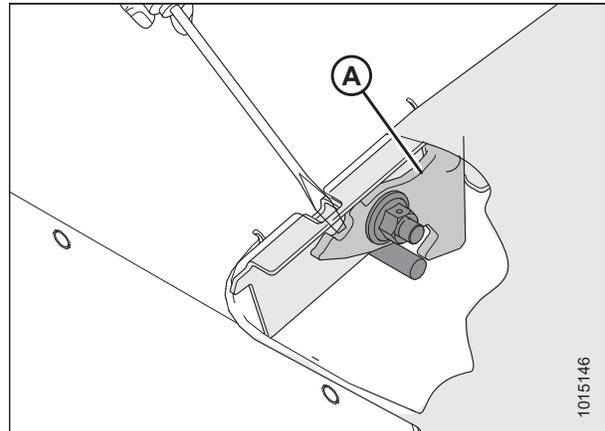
Защелка на дверке ножевого бруса — Местный разрез
